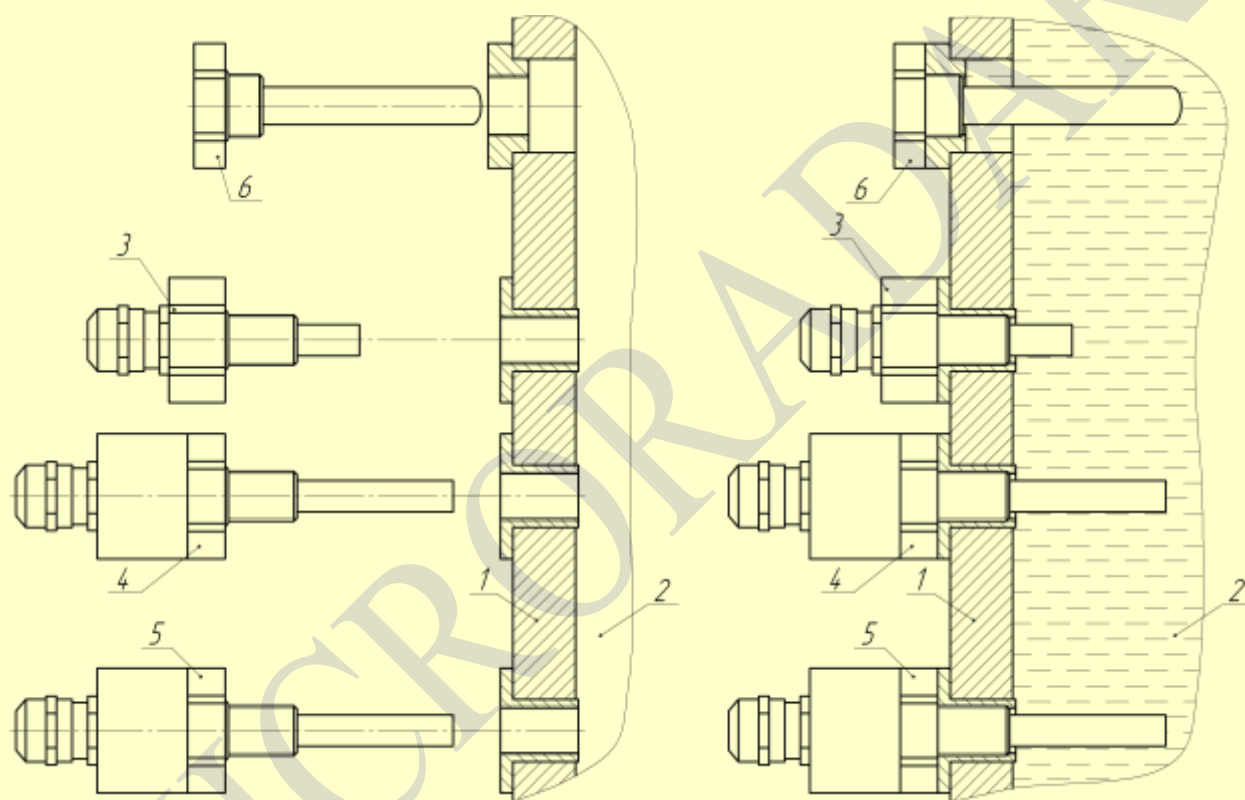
Подготовка к установке блока сенсоров (стрелка указывает направление потока)
